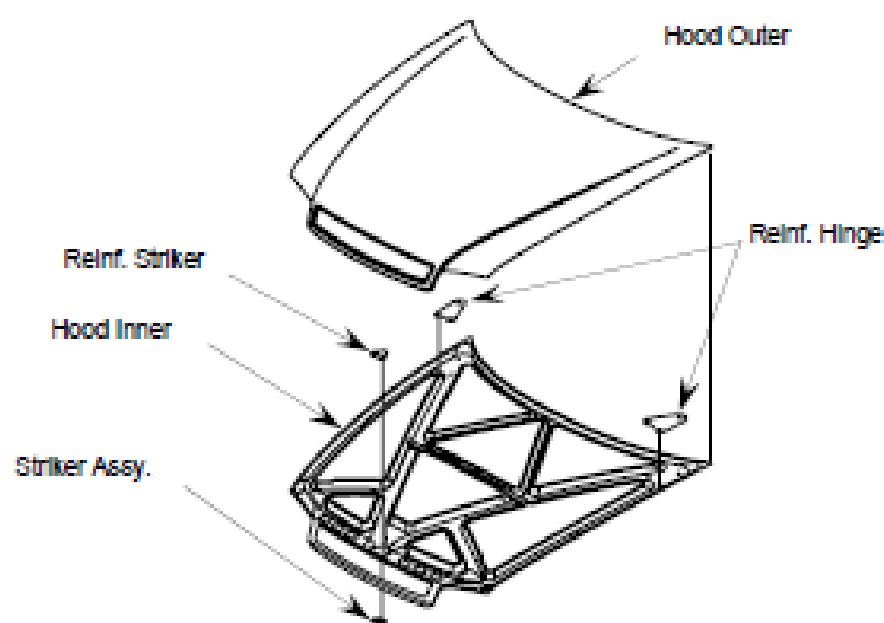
Vista explodida de um capô; a parte interna com reforços é montada com a parte externa. Fonte: Adaptado de Jonkers (2006).
